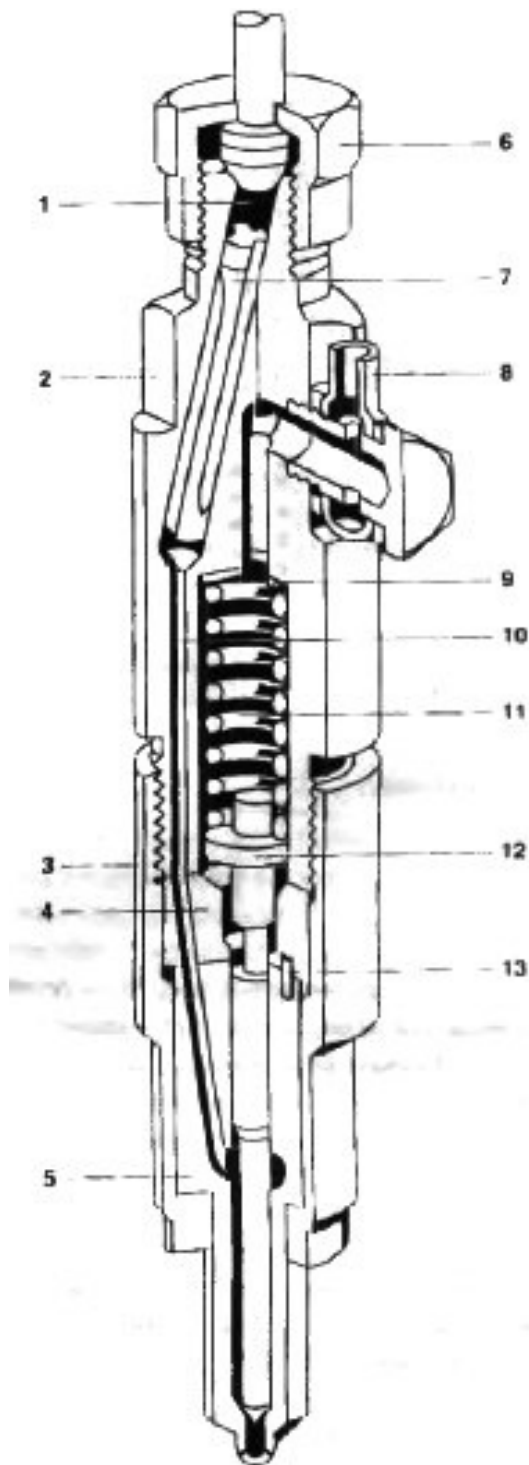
Форсунка: 1 – вхід для палива; 2 – корпус форсунки; 3 – гайка кріплення форсунки; 4 – проміжний елемент; 5 – розпилювач форсунки; 6 – сполучна гайка з паливопроводом високого тиску; 7 – фільтр; 8 – з'єднання для повернення палива; 9 – регулювальні шайби; 10 – канал високого тиску; 11 – натискна пружина; 12 – натискний палець; 13 – штифти для фіксації
